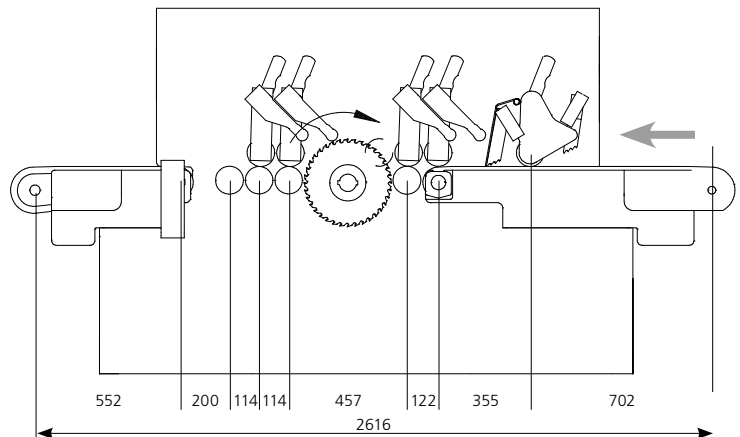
Walzenanordnung K34V/1000 mit Kettenbett
